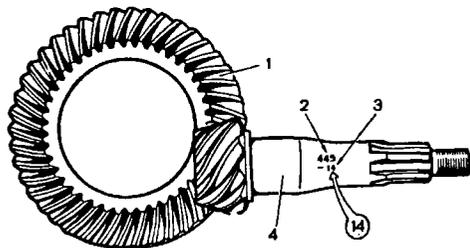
Шестерни главной передачи: 1 - ведомая шестерня; 2 - порядковый номер; 3 - поправка в сотых долях миллиметра к номинальному положению; 4 - ведущая шестерня
